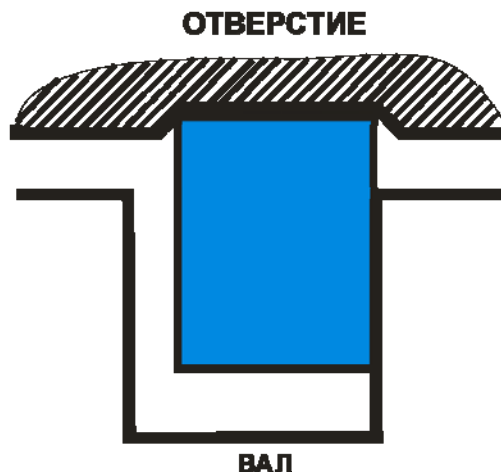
Характерный износ боковой стенки канавки, самого кольца и цилиндрической поверхности отверстия
